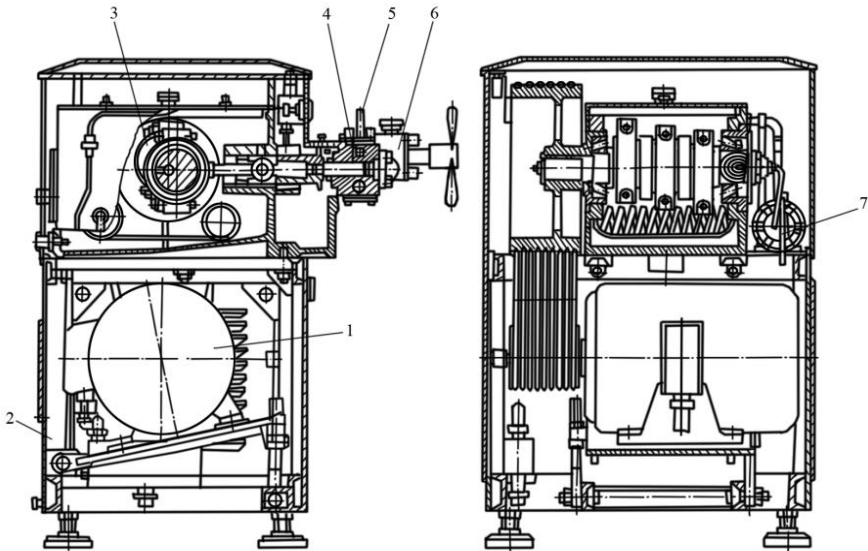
Гомогенізатор А1-ОГМ: 1 – електродвигун; 2 – станина; 3 – кривошипно-шатунний механізм; 4 – плунжерний блок; 5 – манометрична головка; 6 – гомонізуюча головка; 7 – система мащення
